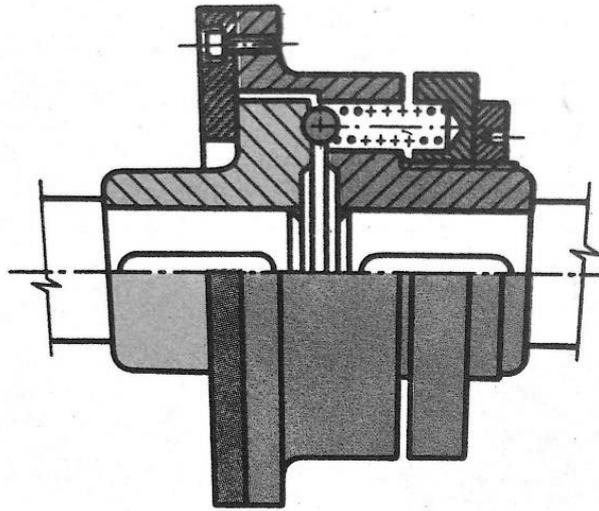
Pojistná spojka se střížnými kolíky [8].
